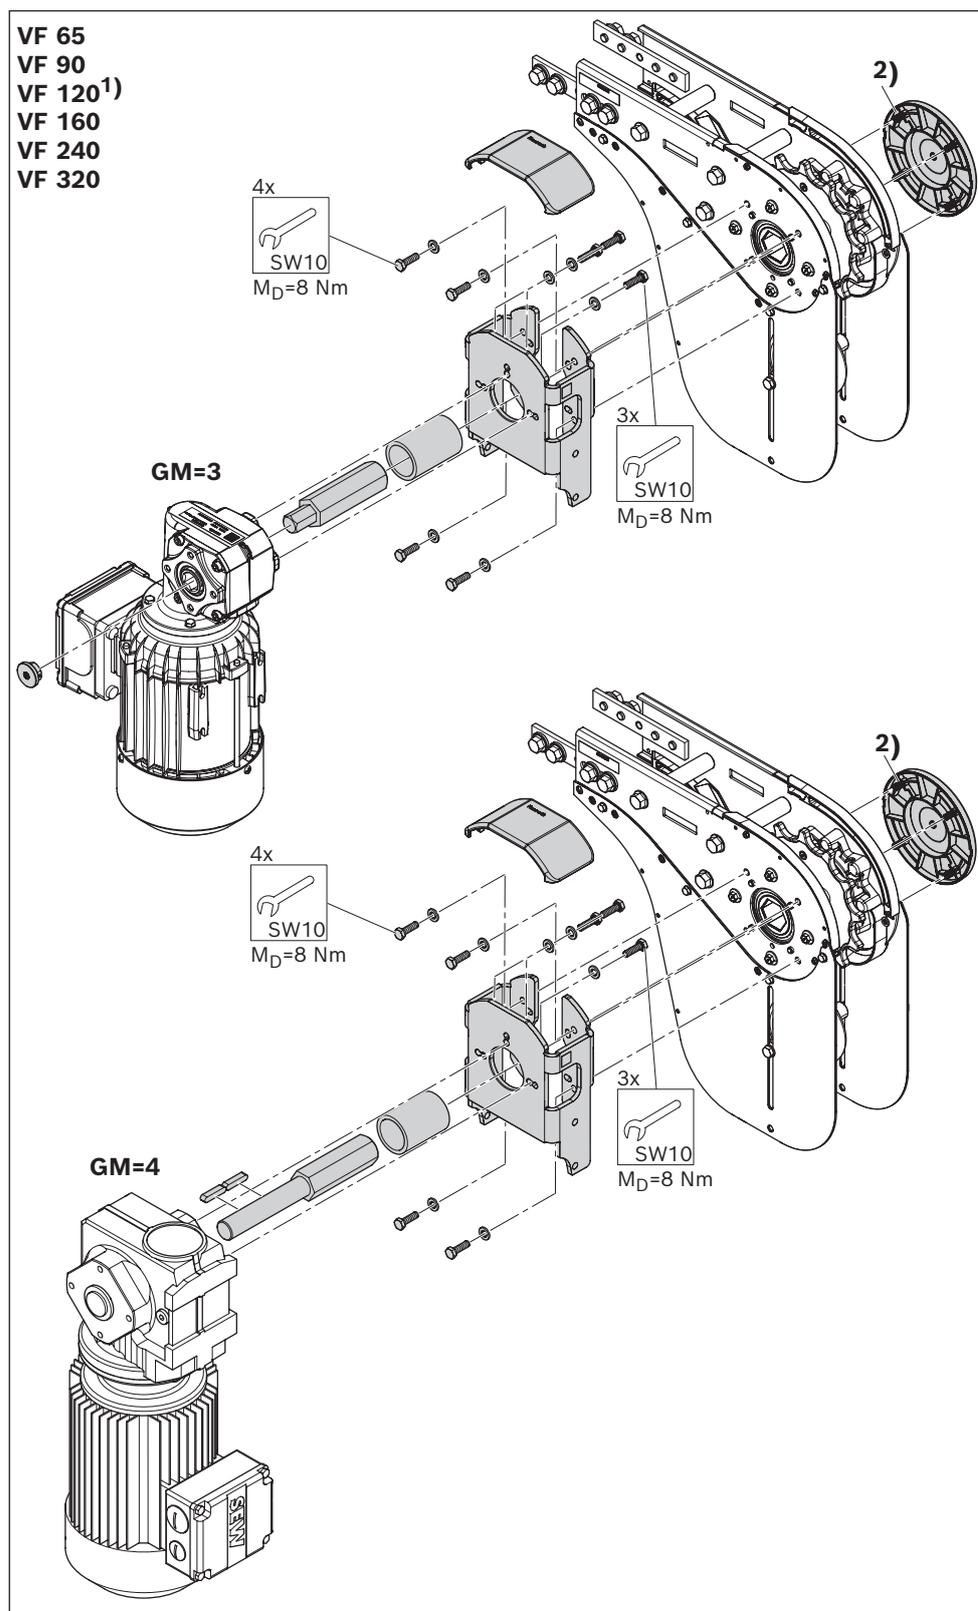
Unità di base, sistema STS, montaggio del motoriduttore GM = 3/4 STS a flangia
